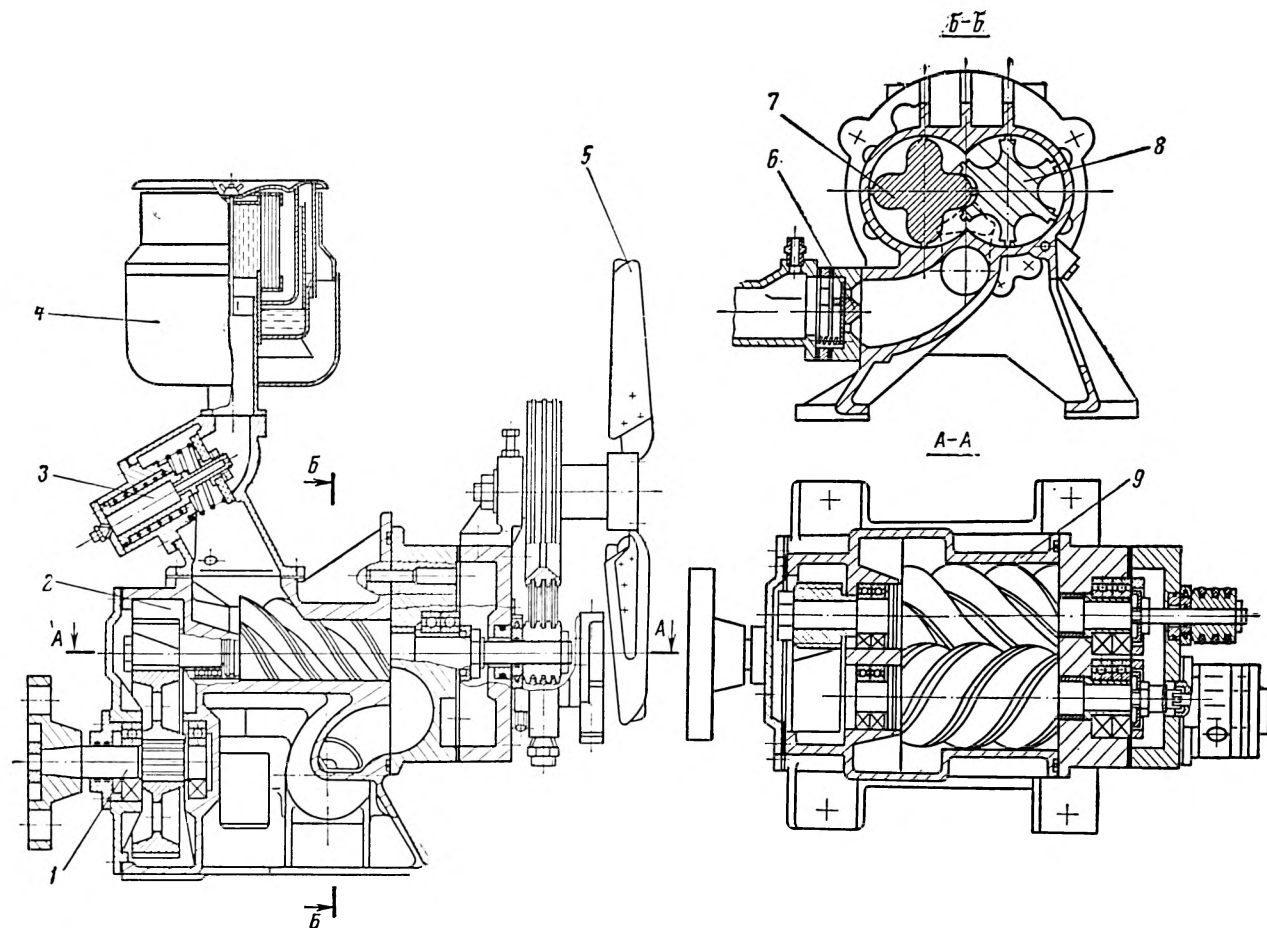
Передвижной компрессор ЗИФ-ШВ-5
